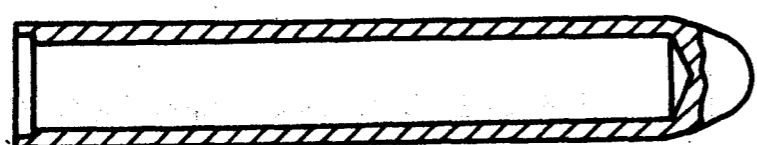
Оправка 7820-5053 для установки резиновых сальников амортизаторов
